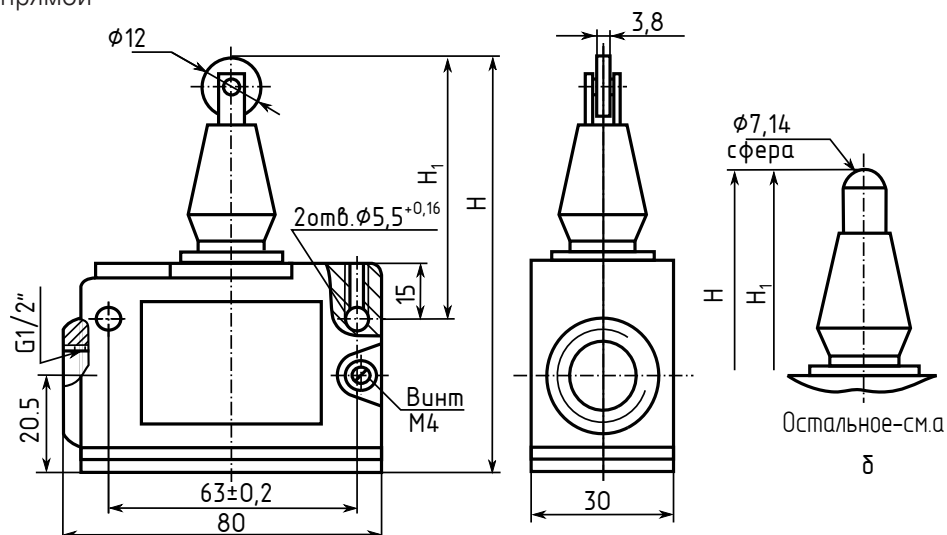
Габаритные, установочные и присоединительные размеры микровыключателей со степенью защиты IP54 с комбинированным креплением на поверхности, с монтажом проводов винтами или пайкой с приводом:
